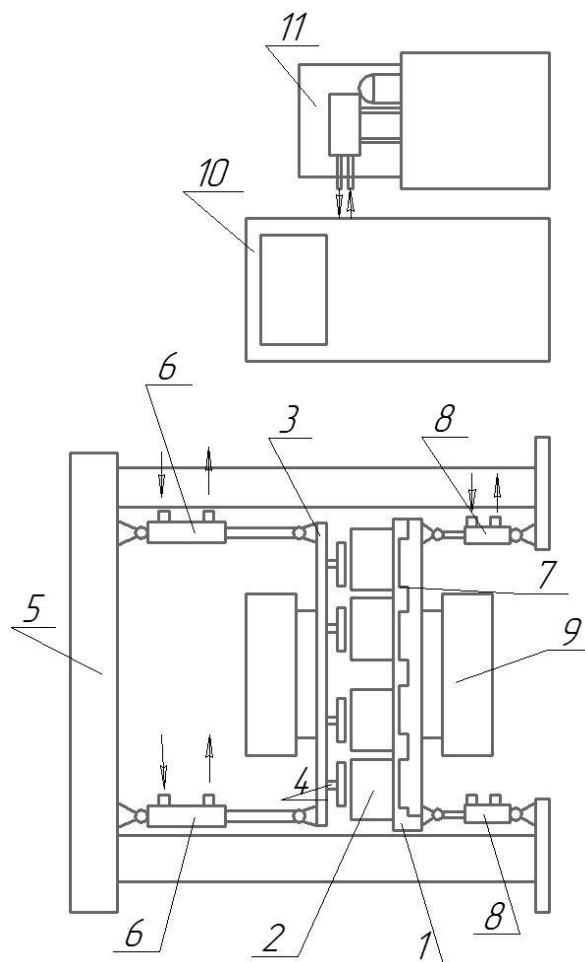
Принципова схема машини для напівсухого пресування з дебалансним приводом
